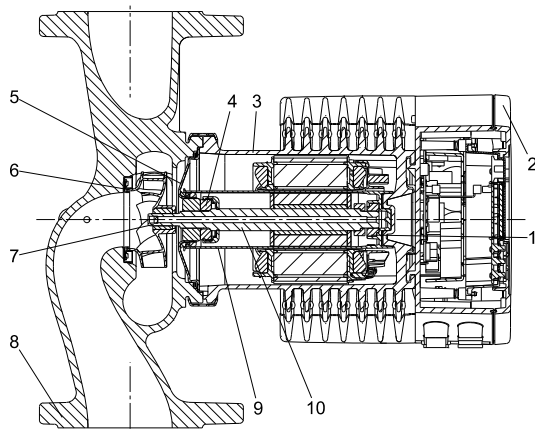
Модификация с фланцами и корпусом ротора из ПФС
